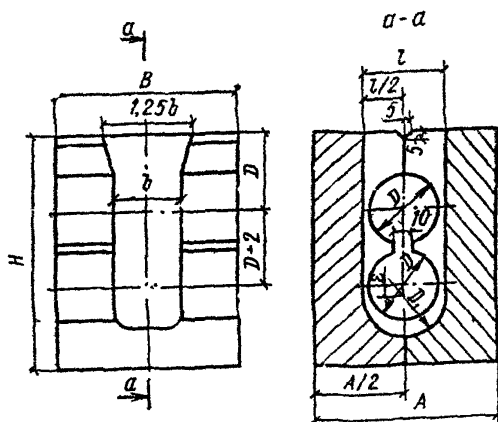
Конструкция инвентарной формы для сварки стыковых соединений спаренных стержней.
